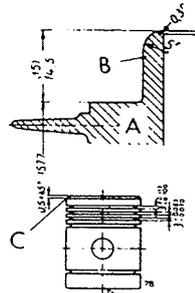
Merkmale von Zylinder und Kolben früherer Ausführung
